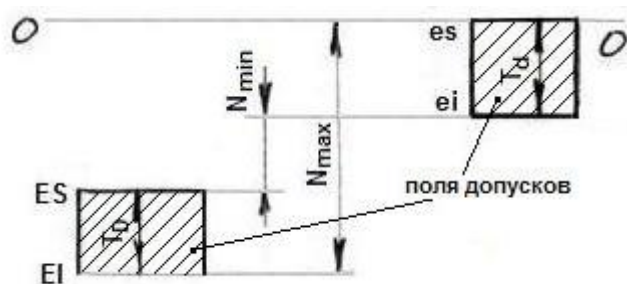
Схема полей допусков для посадки с натягом
